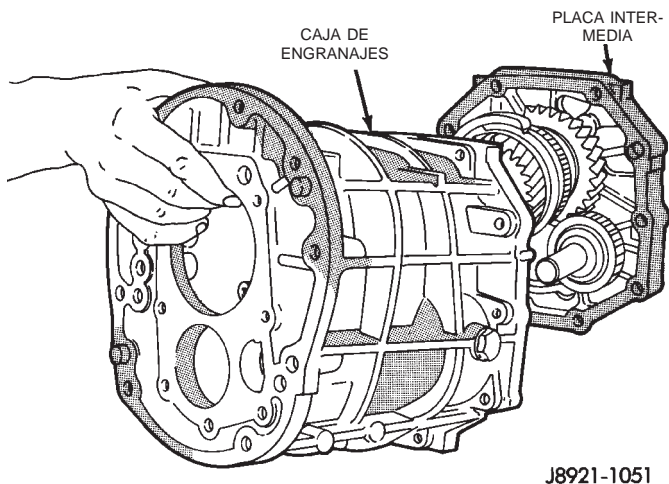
Instalación de la caja de engranajes de la transmisión en la placa intermedia
